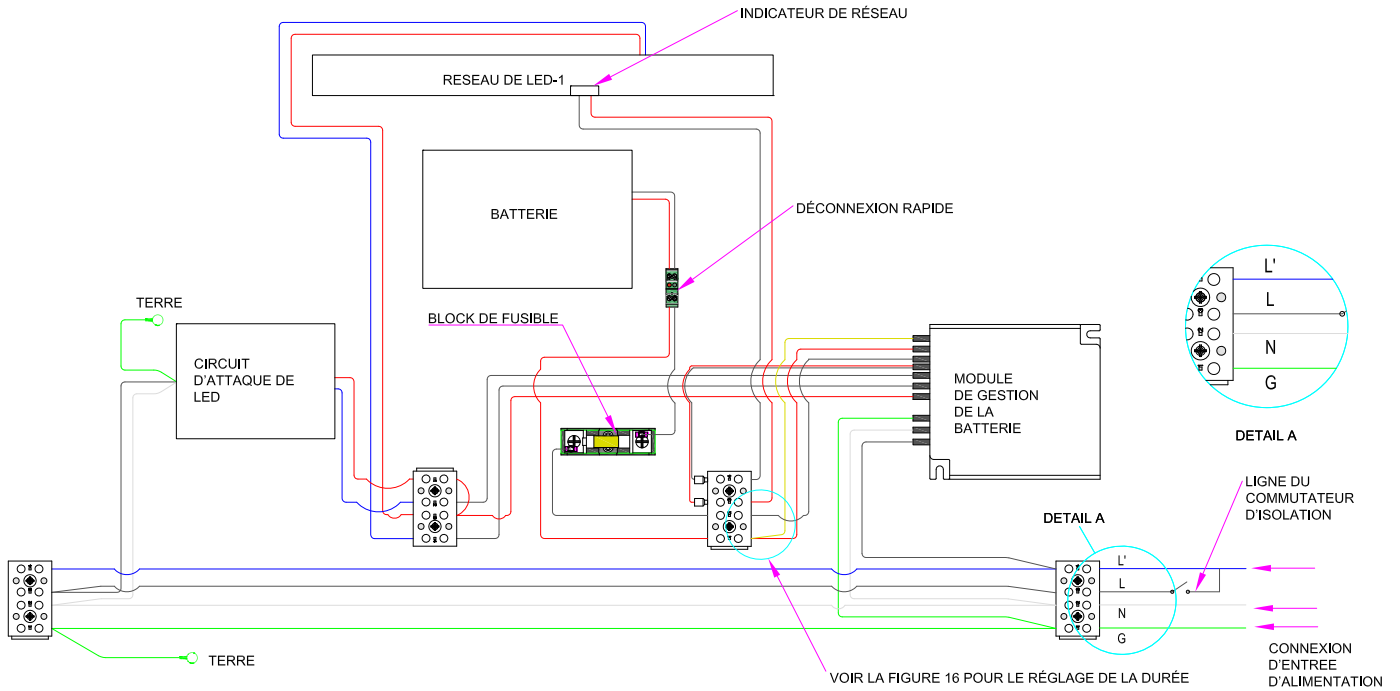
A: CABLAGE STANDARD, DISPOSITION DE CONNEXION A 4 FILS AVEC BORNES A VIS FIXES: 2 PIEDS
